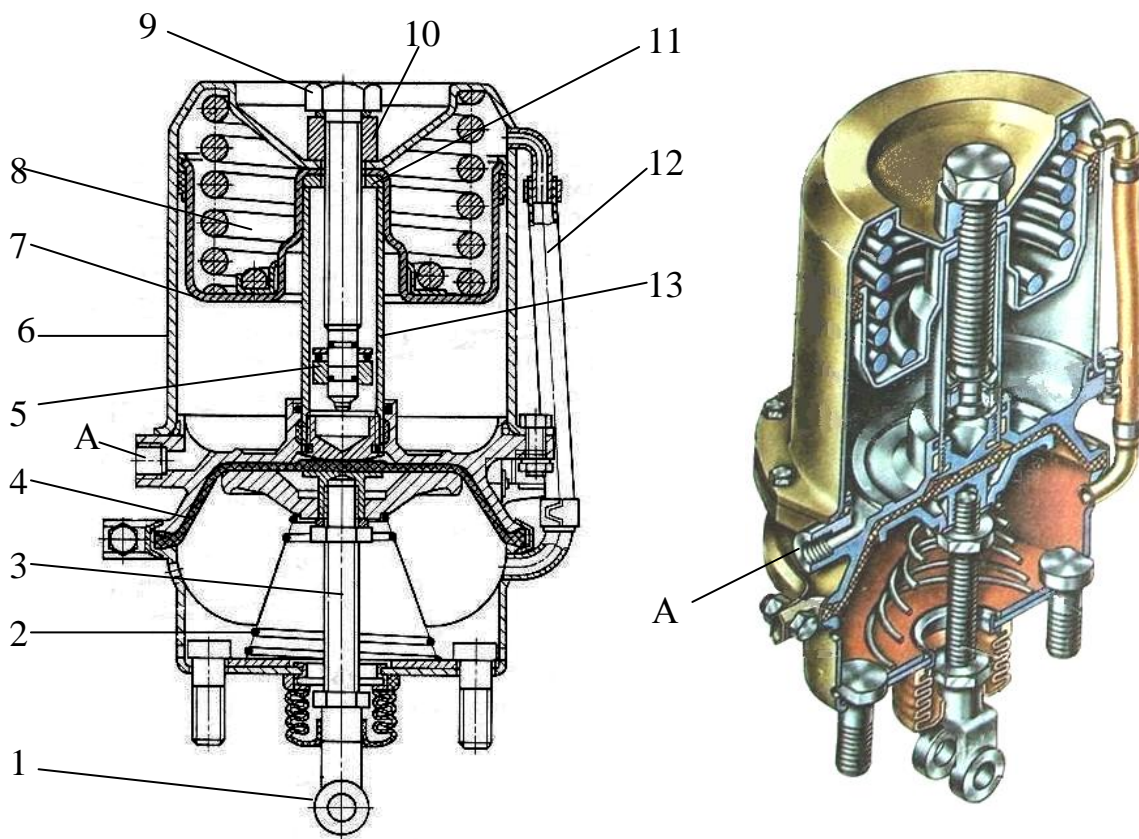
Тормозная камера типа 20 с энергоаккумулятором для колес задней тележки автомобиля-тягача КАМАЗ: 1 – вилка; 2 и 8 – пружины; 3 – шток; 4 – мембрана; 5 – подшипник; 6 – цилиндр; 7 – поршень; 8 – рычаг; 9 – винт; 10 – неподвижная гайка; 11 – упорная шайба; 12 – соединительная трубка; 13 – толкатель; А – вывод в контур № 3 привода тормозов стояночной и запасной тормозных систем
